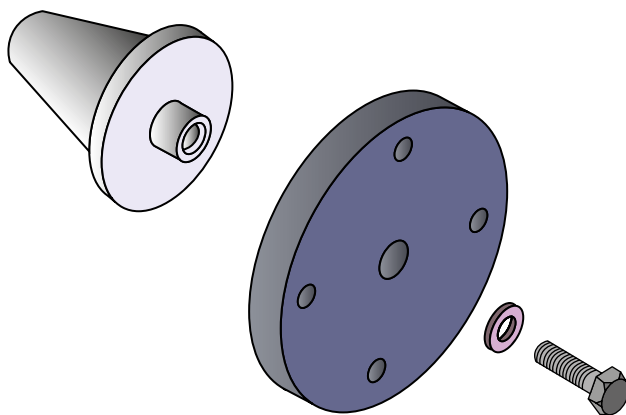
Dispositivo para torno explosionado (despiece)
